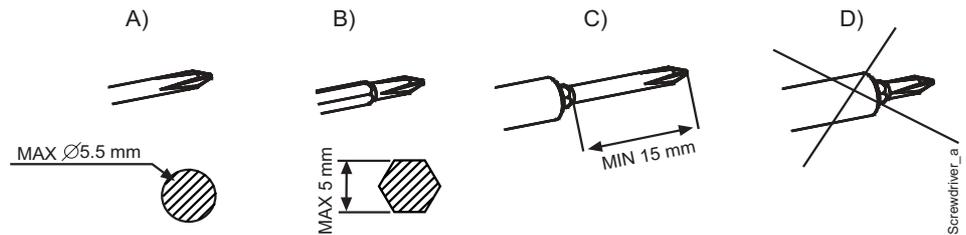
1 Destornillador y accesorio para terminales CT de tipo tornillo de compresión
